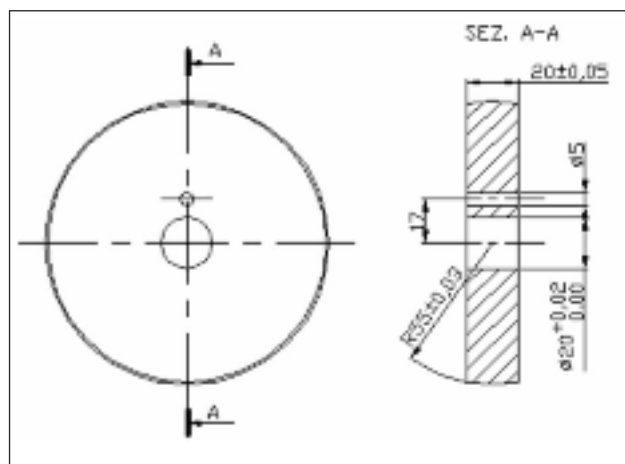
Geometria e dimensioni del disco di prova. Disc specimen geometry.
